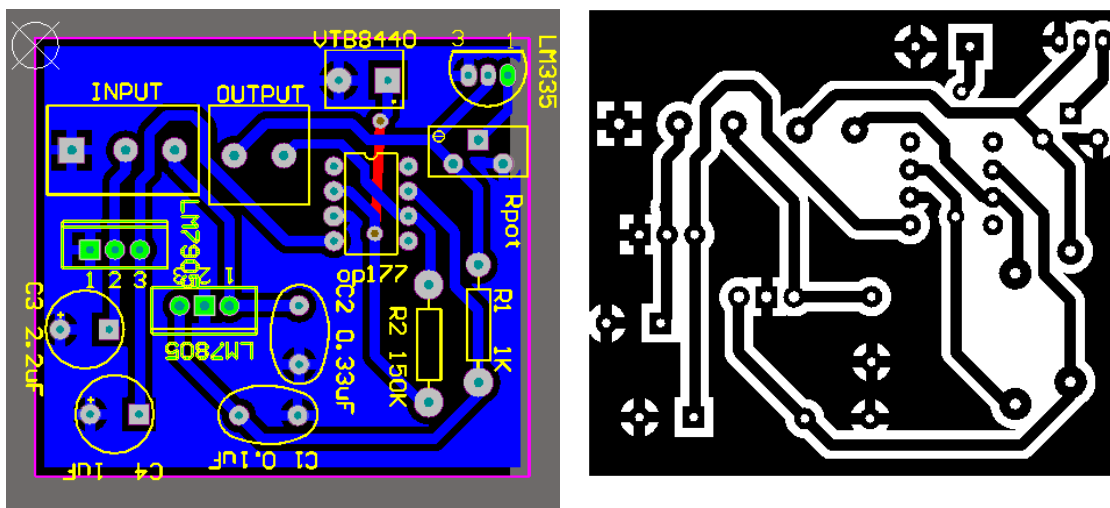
PCB sonda diseño cara inferior y fotolito
